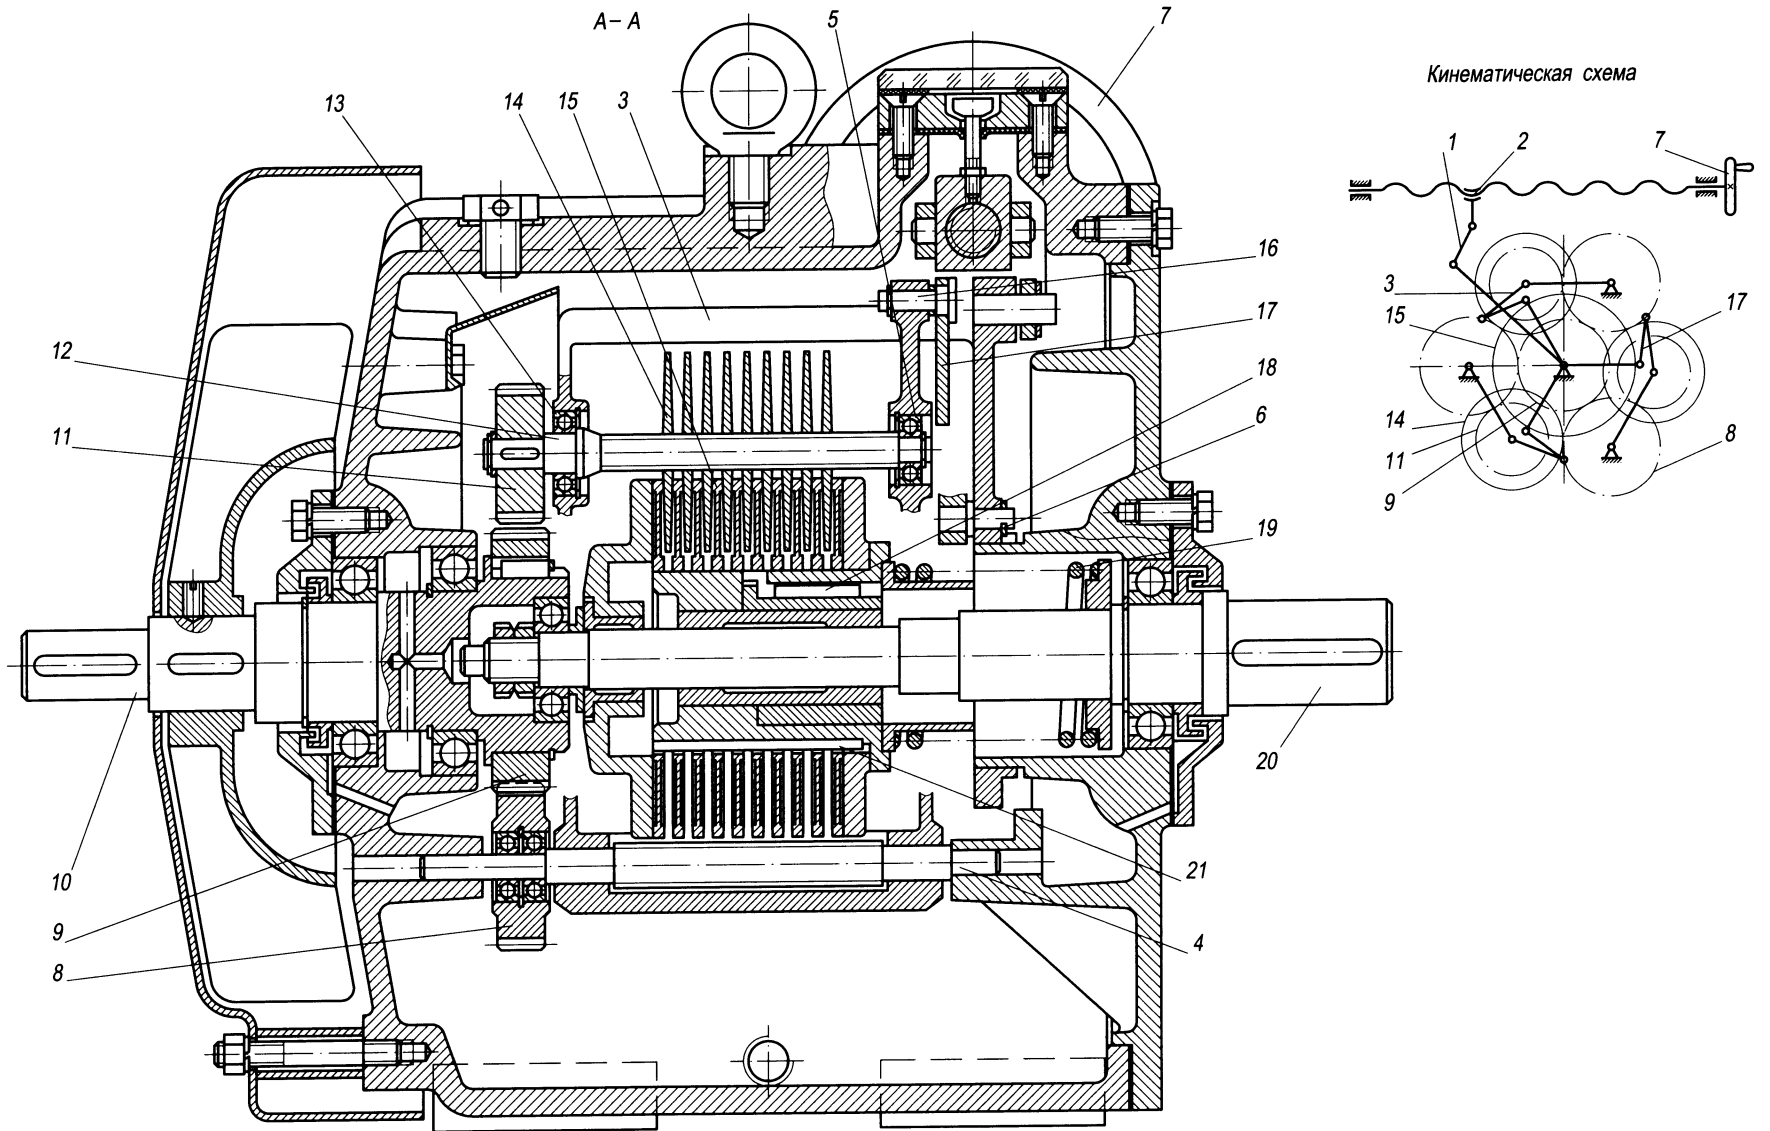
Вариатор конструкции ВНИИРедуктор (окончание):
